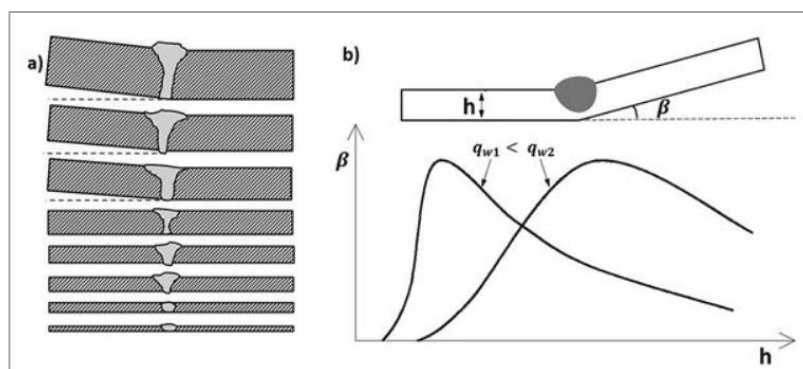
Deformações de uma chapa de aço em soldadura topo a topo, mediante diferentes espessuras
